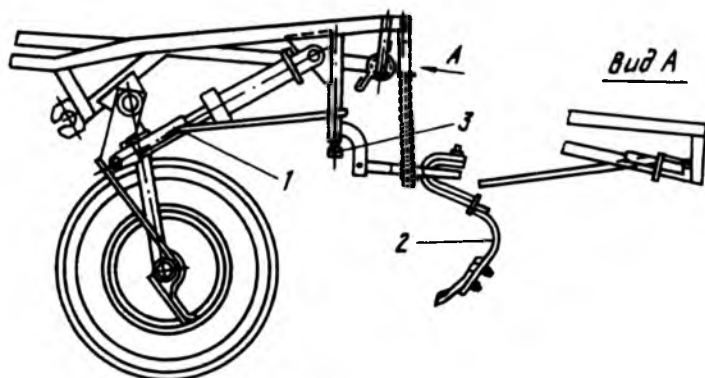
Установка предохранительного упора и рыхлительной лапы у сажалки САЯ-4:
